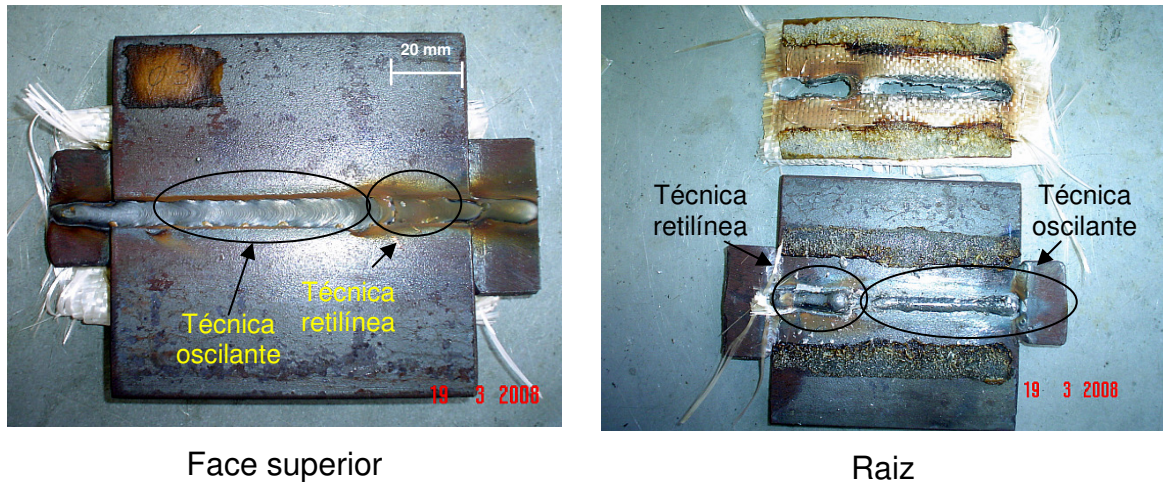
Mudança de técnica de soldagem de retilínea para com pequena oscilação (junta 03)
